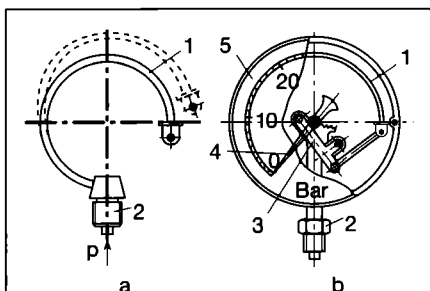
Manometru Indicator cu tub flexibil:
